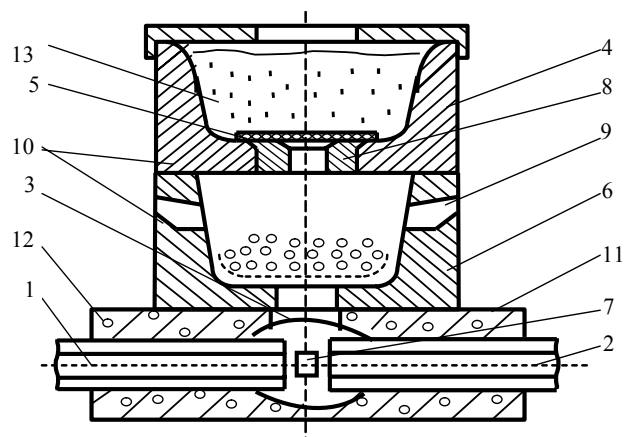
Схема проведення зварювання двох заготовок з високомарганцевої сталі:
